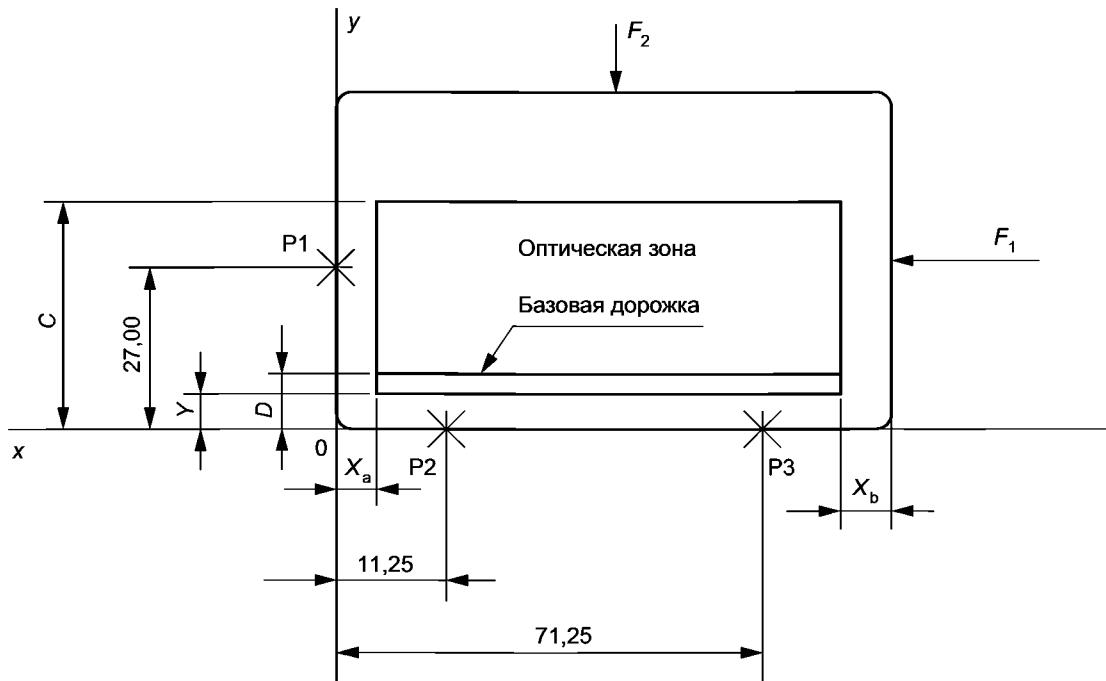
Расположение оптической зоны и базовой дорожки
